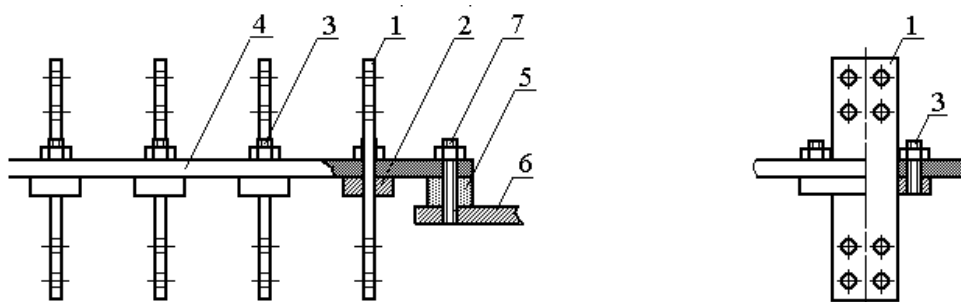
Шинный ввод и его крепление на крышке бака трансформатора
